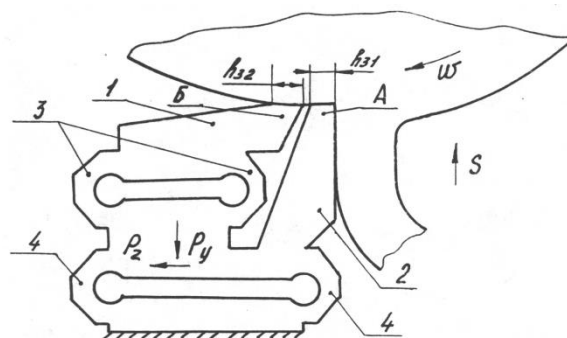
Схема расположения пластин А и Б разрезного резца при установке СТДРР на горизонтально-фрезерном станке для исследования распределения контактных нагрузок на фаске задней поверхности резца
